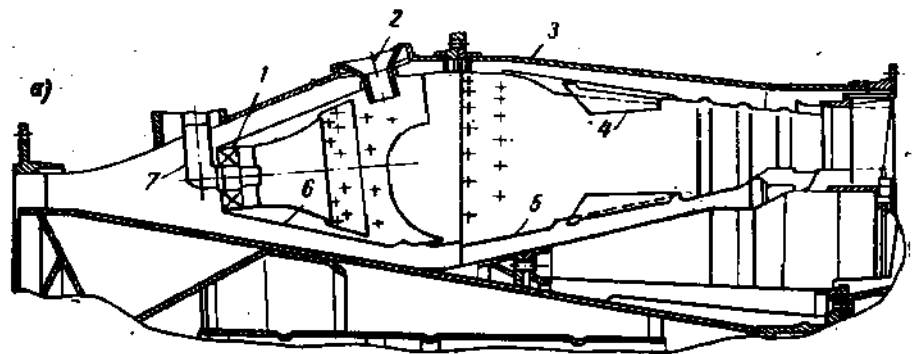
Кільцева камера згорання (двигун НК-12): 1 - завихритель потоку повітря; 2 - фіксатор жарової труби; 3 - зовнішній корпус; 4 - змішувач; 5 - кільцева жарова труба; 6 - фронтове пристрій; 7 - форсунка
